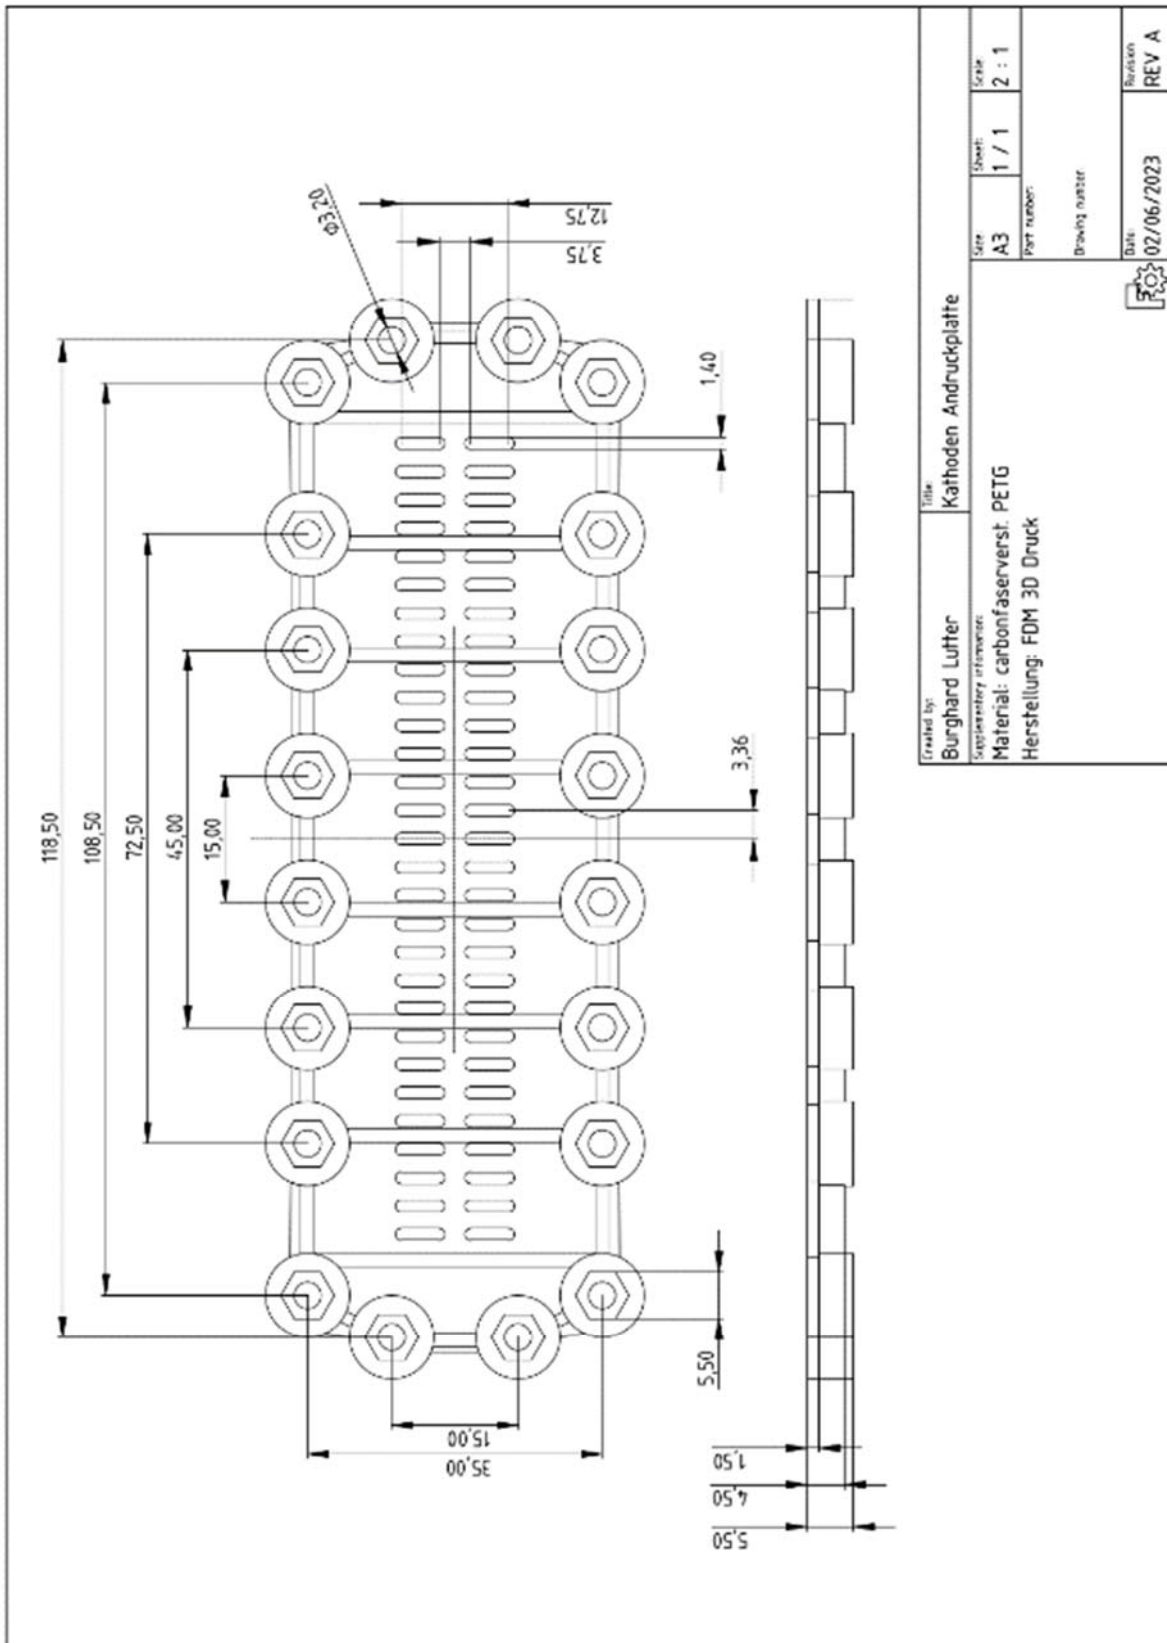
Technische Zeichnung der Kathoden Andruckplatte
